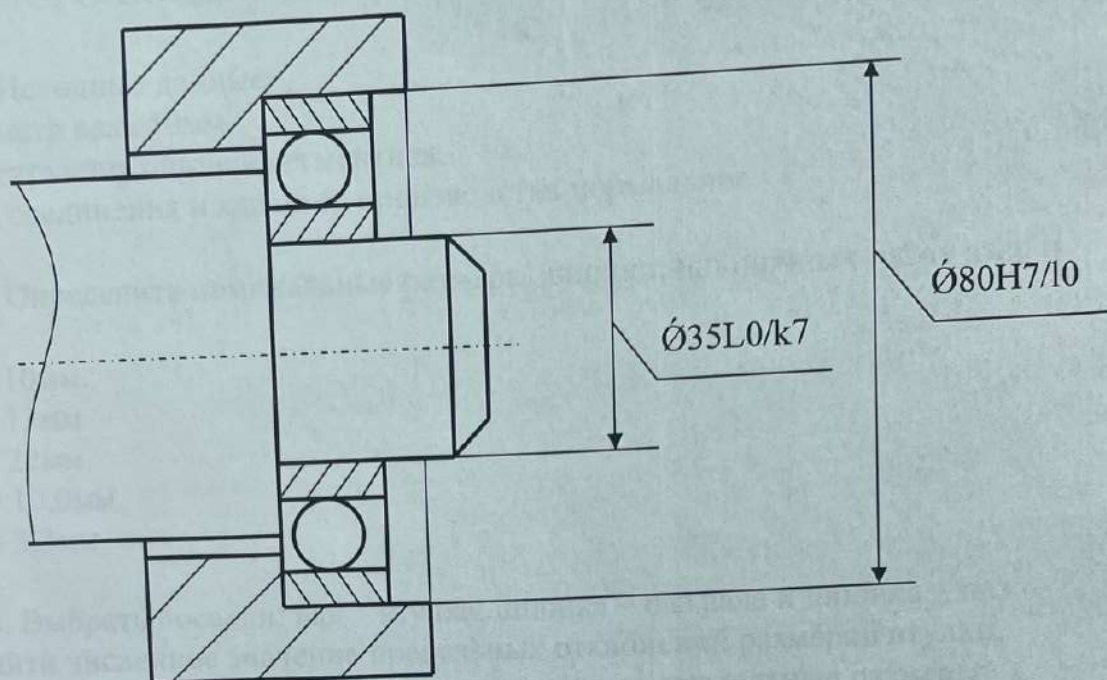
в - Эскиз соединения в сборе для подшипникового узла.
